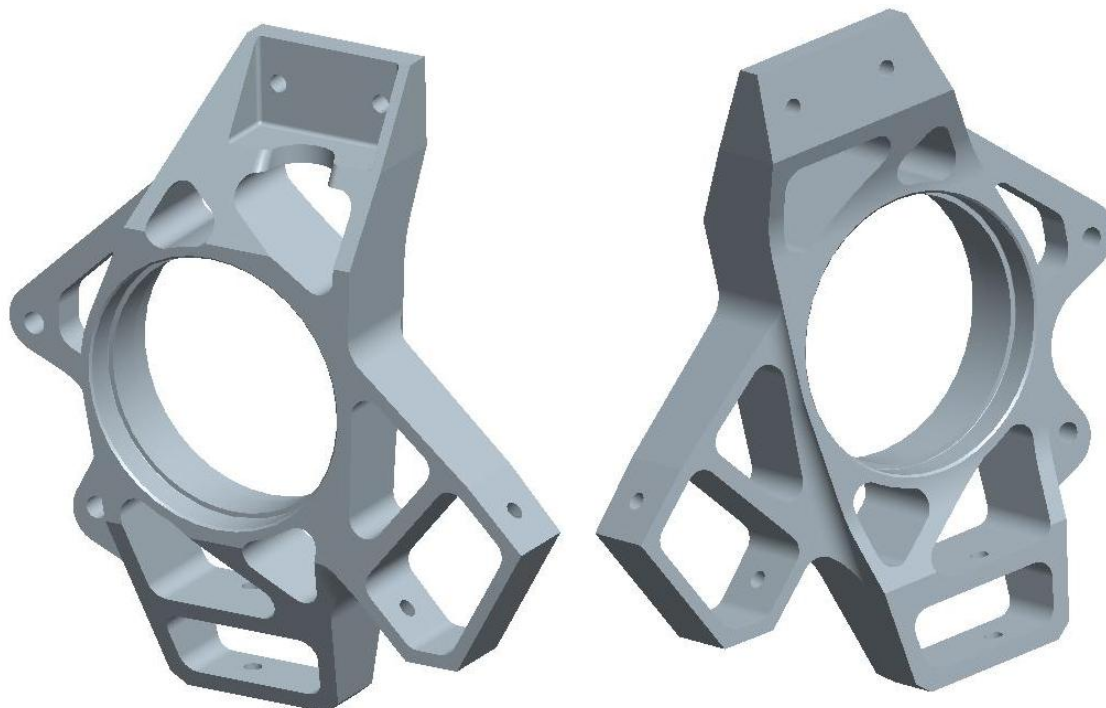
Přední těhlice s brzdovým třmenem – druhá varianta
